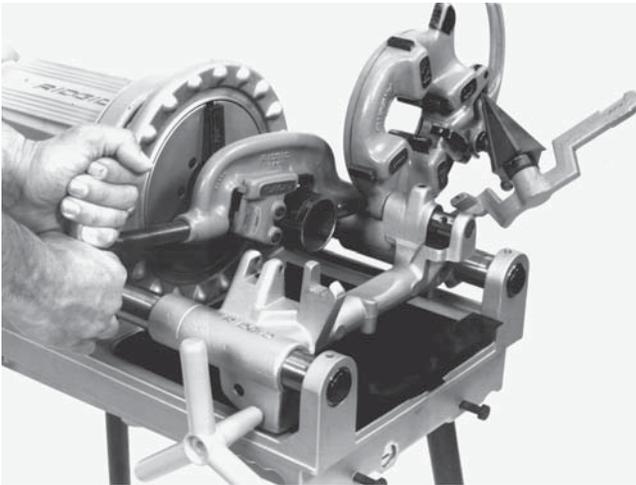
Обрезка трубы с помощью станка 300 compact
